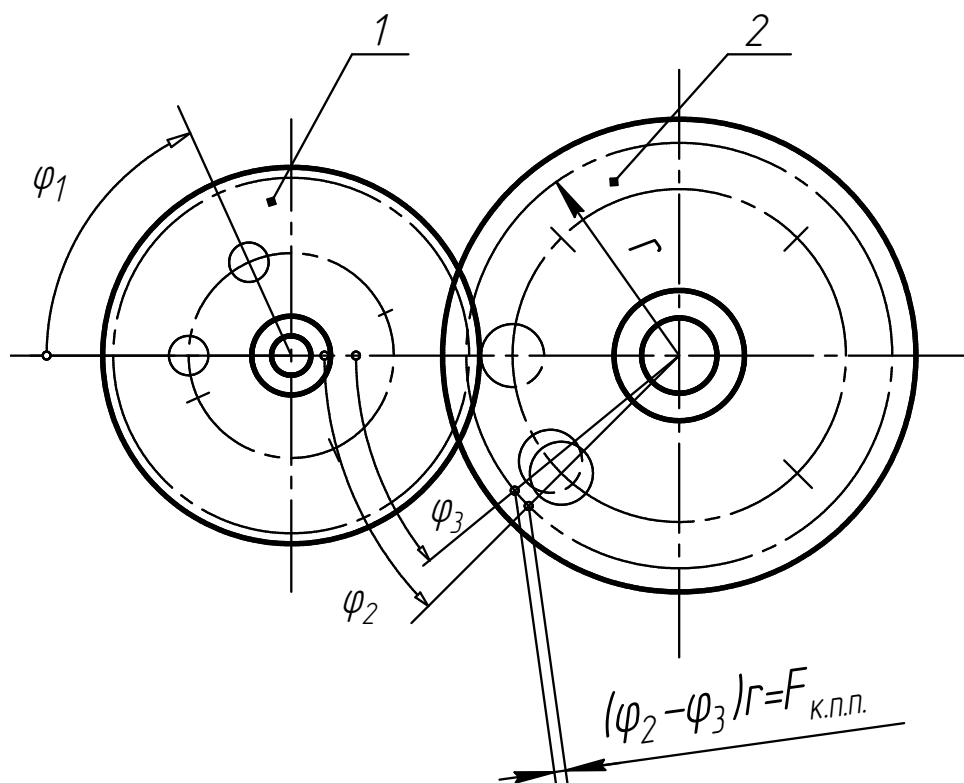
Схема определения кинематической погрешности зубчатой передачи
